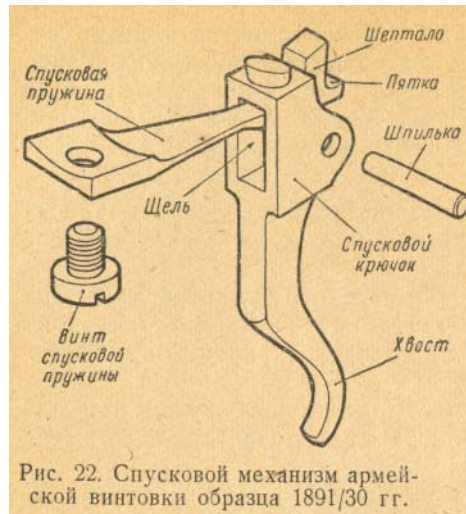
Спусковой механизм армейской винтовки образца 1891/30 гг.
